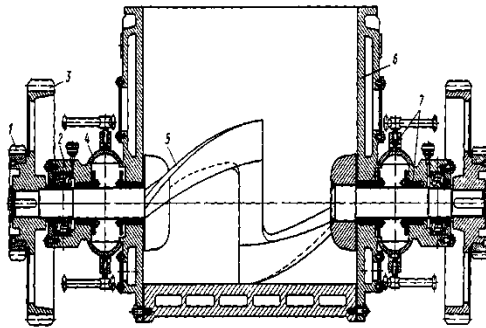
Приклад конструкції ротора із Z-подібними лопатями: 1 – мале зубчасте колесо; 2 – підшипник; 3 – велике зубчасте колесо; 4 – сальникова коробка; 5 – лопать; 6 – бокова стінка; 7 – сальникове ущільнення
